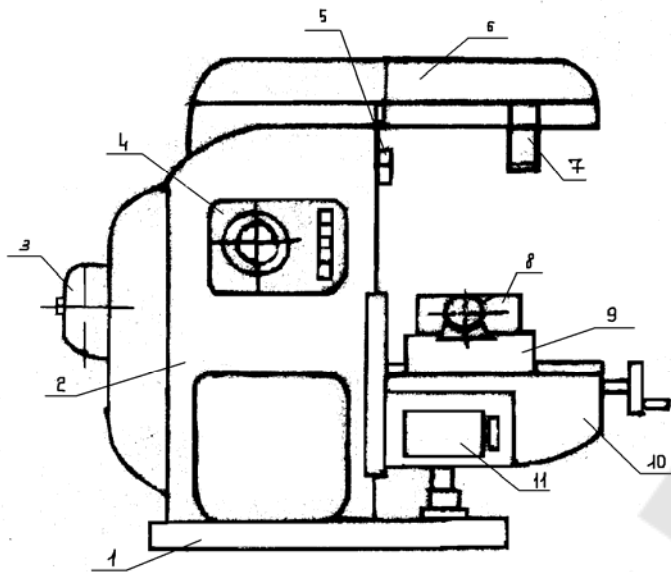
Общий вид горизонтально-фрезерного станка модели 6P81.
